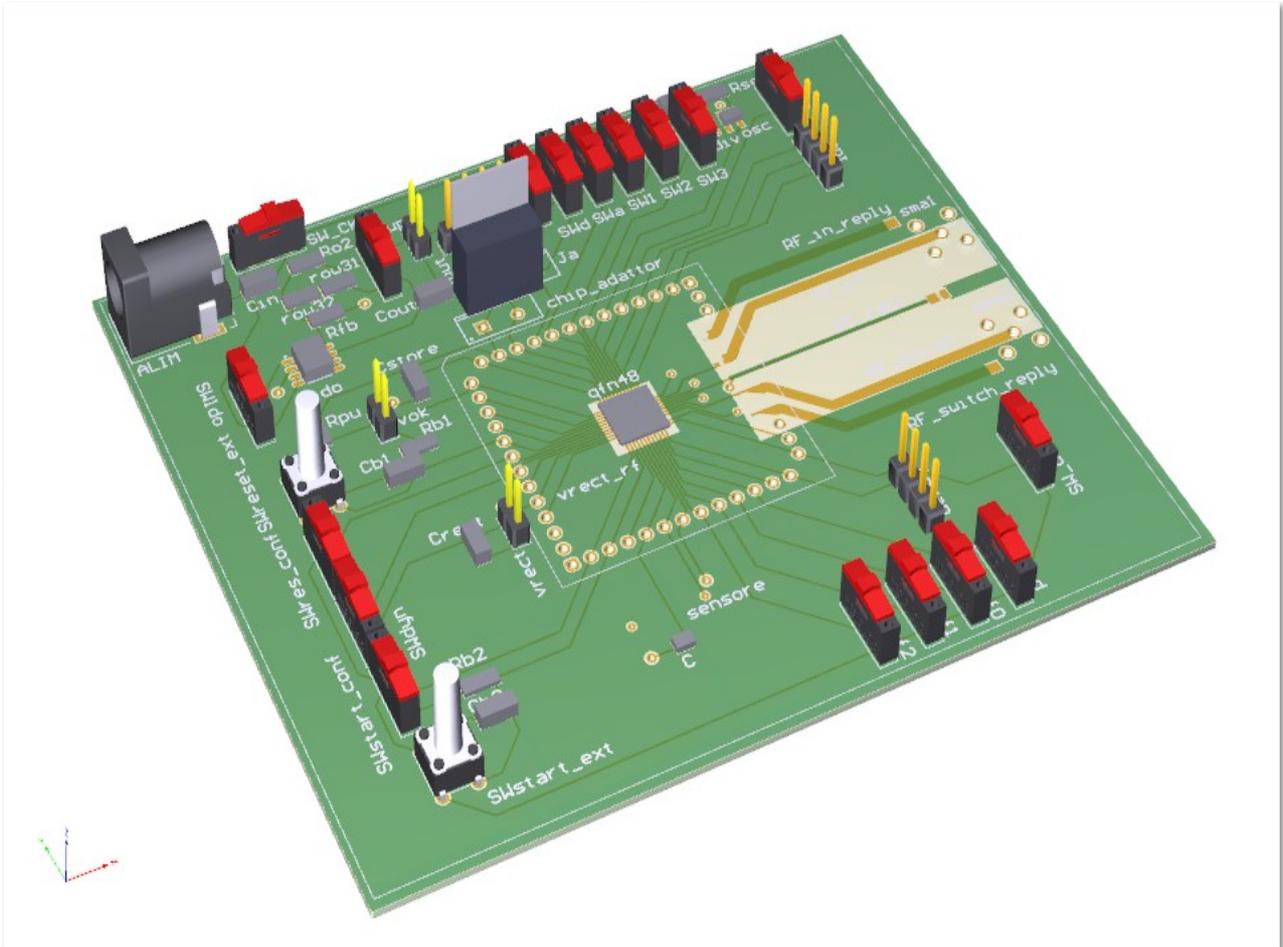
Visione in 3d del pcb(Altium Designer)
